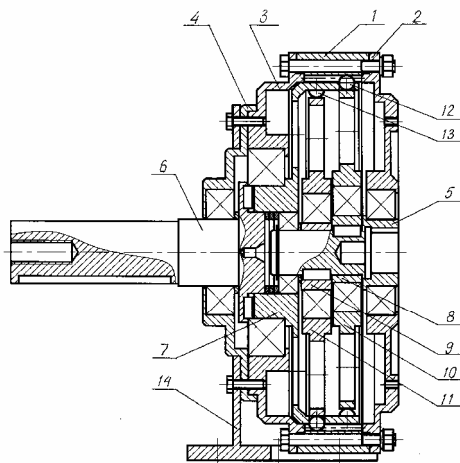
Редуктор привода станка для монтажа автомобильных шин
